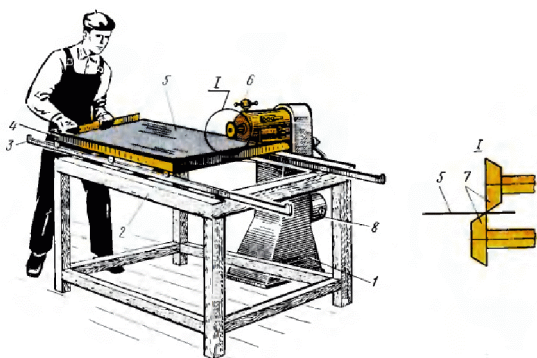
Обрезной станок конструкции И. П. Прохорова:
